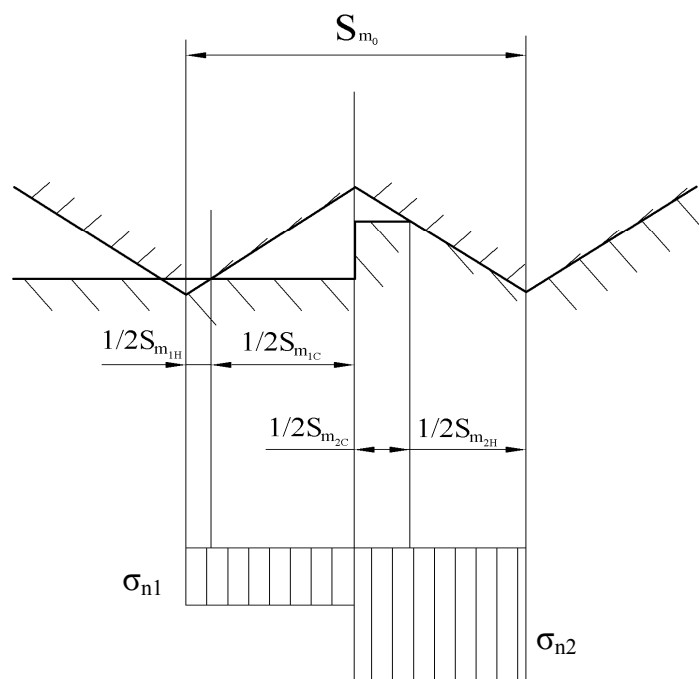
Вдавливание шероховатой поверхности валка в замороженную корку металла
